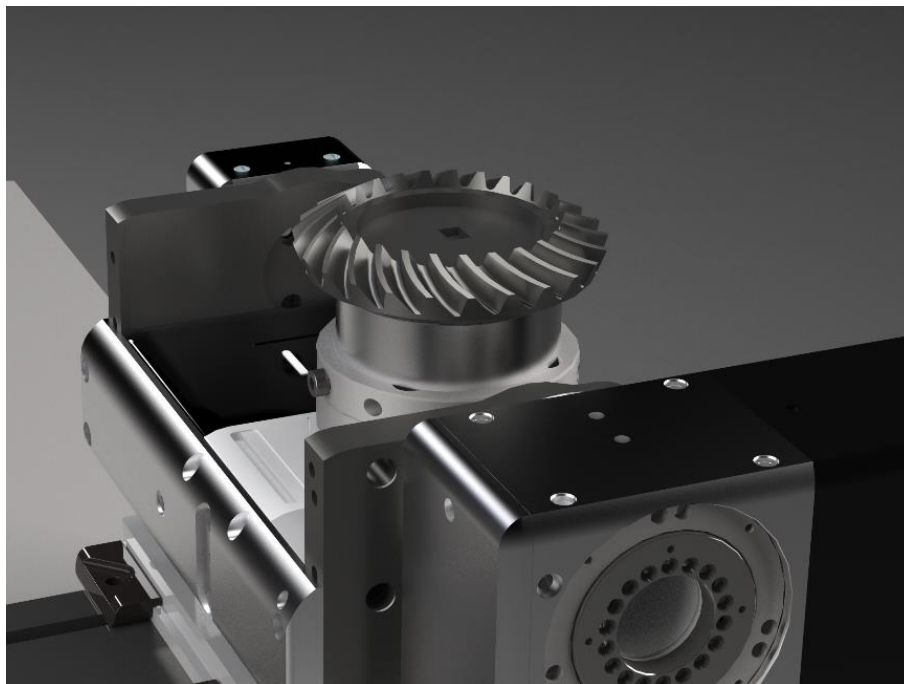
Disposición de la configuración del Demostrador II durante el mecanizado.
